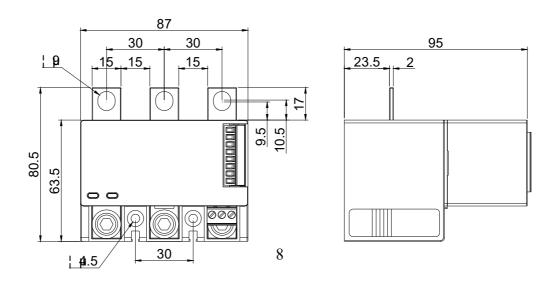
Внешний вид и габаритные размеры КСМ-М4-250
